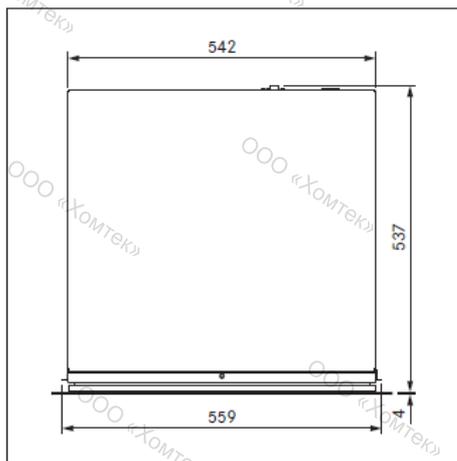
Размеры прибора, модель MSS290, вид сверху
